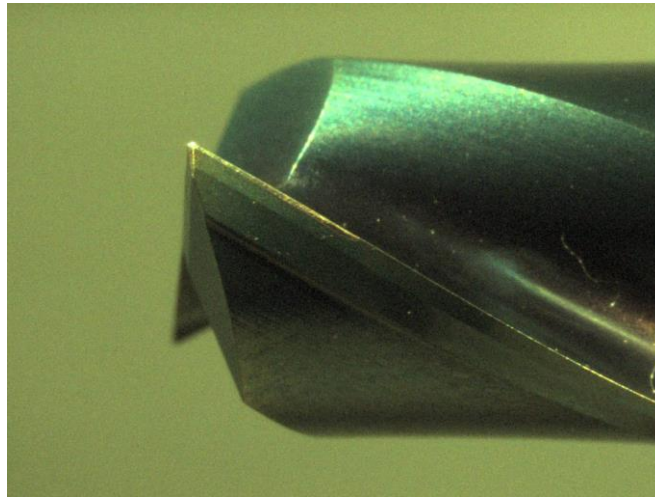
Testovaná fréza před experimentem bez opotřebení
